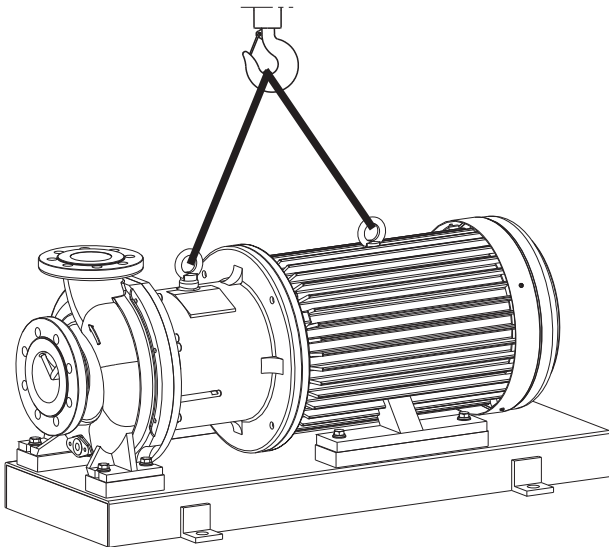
Hebezeug an der Blockpumpe befestigen (Prinzipbild)
